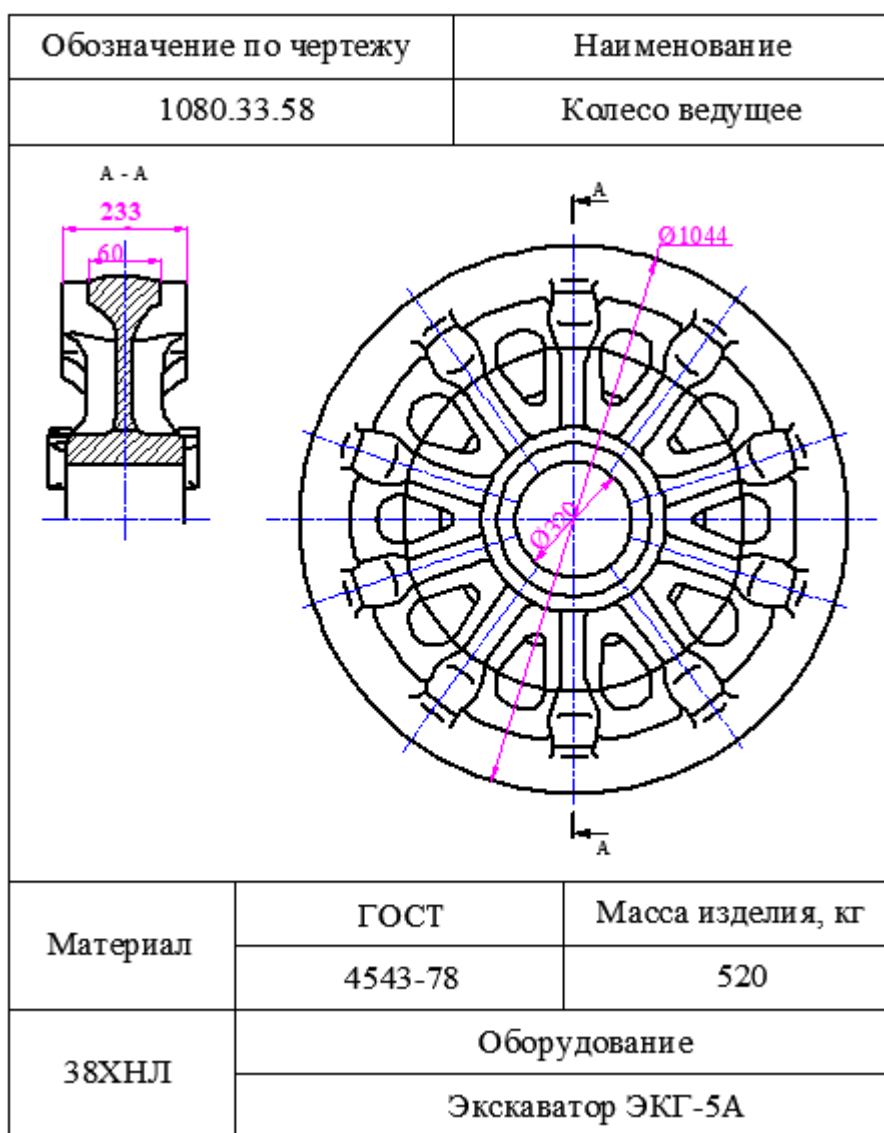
чертеж ведущего колеса экскаватора ЭКГ-5А
